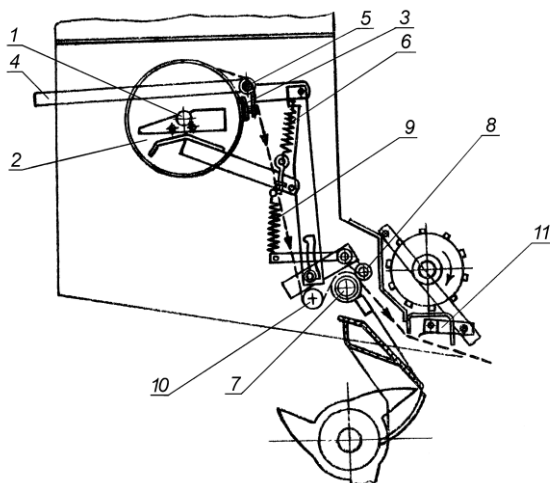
Механизм обмотки рулона сеткой: 1 – приемник бобины сетки; 2 – тормозной диск; 3 – тормоз сетки; 4 – рычаг; 5 – вал; 6 – пружина тормоза; 7 – обрезиненный вал; 8 – прижимной ролик; 9 – пружина прижимного ролика; 10 – держатель сетки; 11 – нож.
